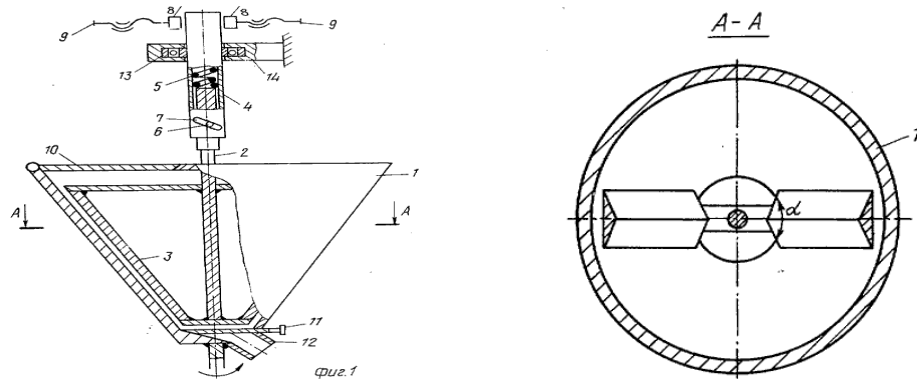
Відцентрова установка для абразивної обробки деталей різної форми:
